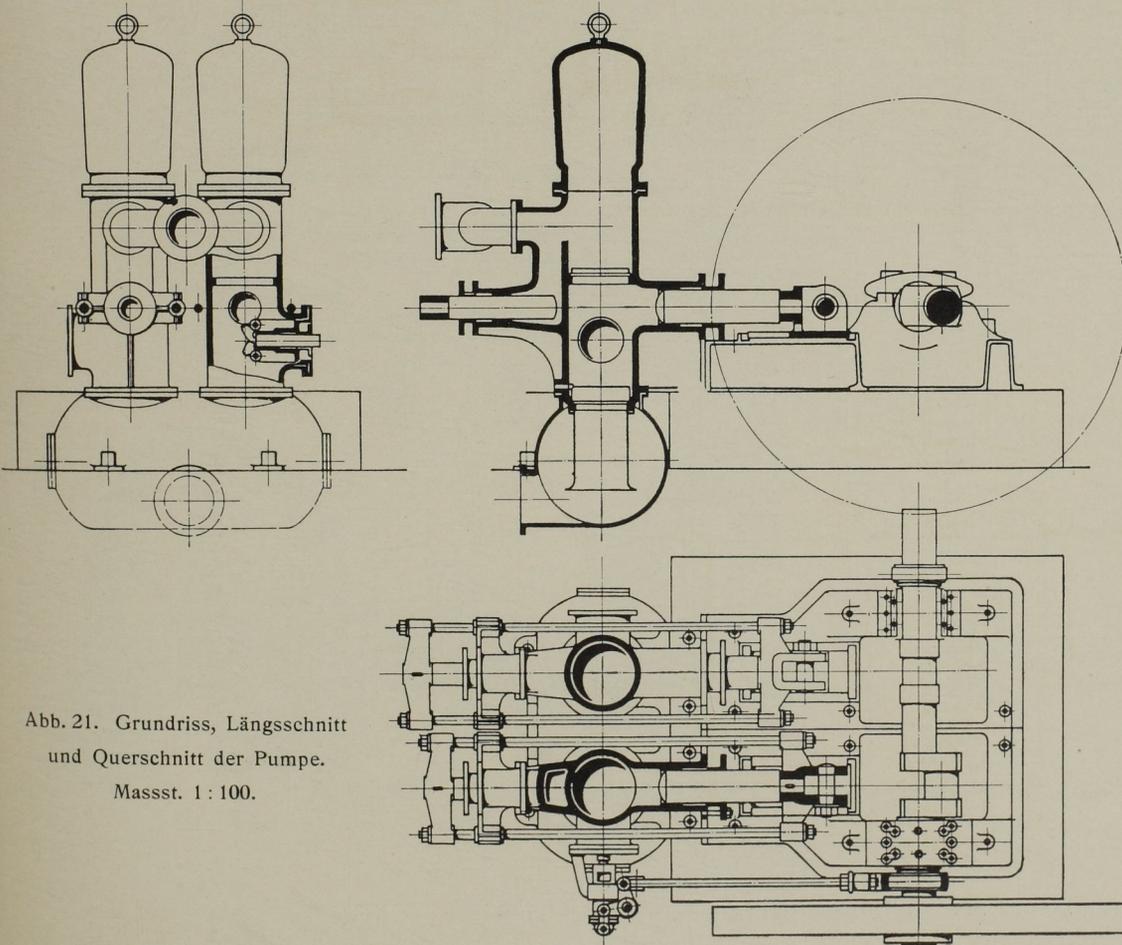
Grundriss, Längsschnitt und Querschnitt der Pumpe.
